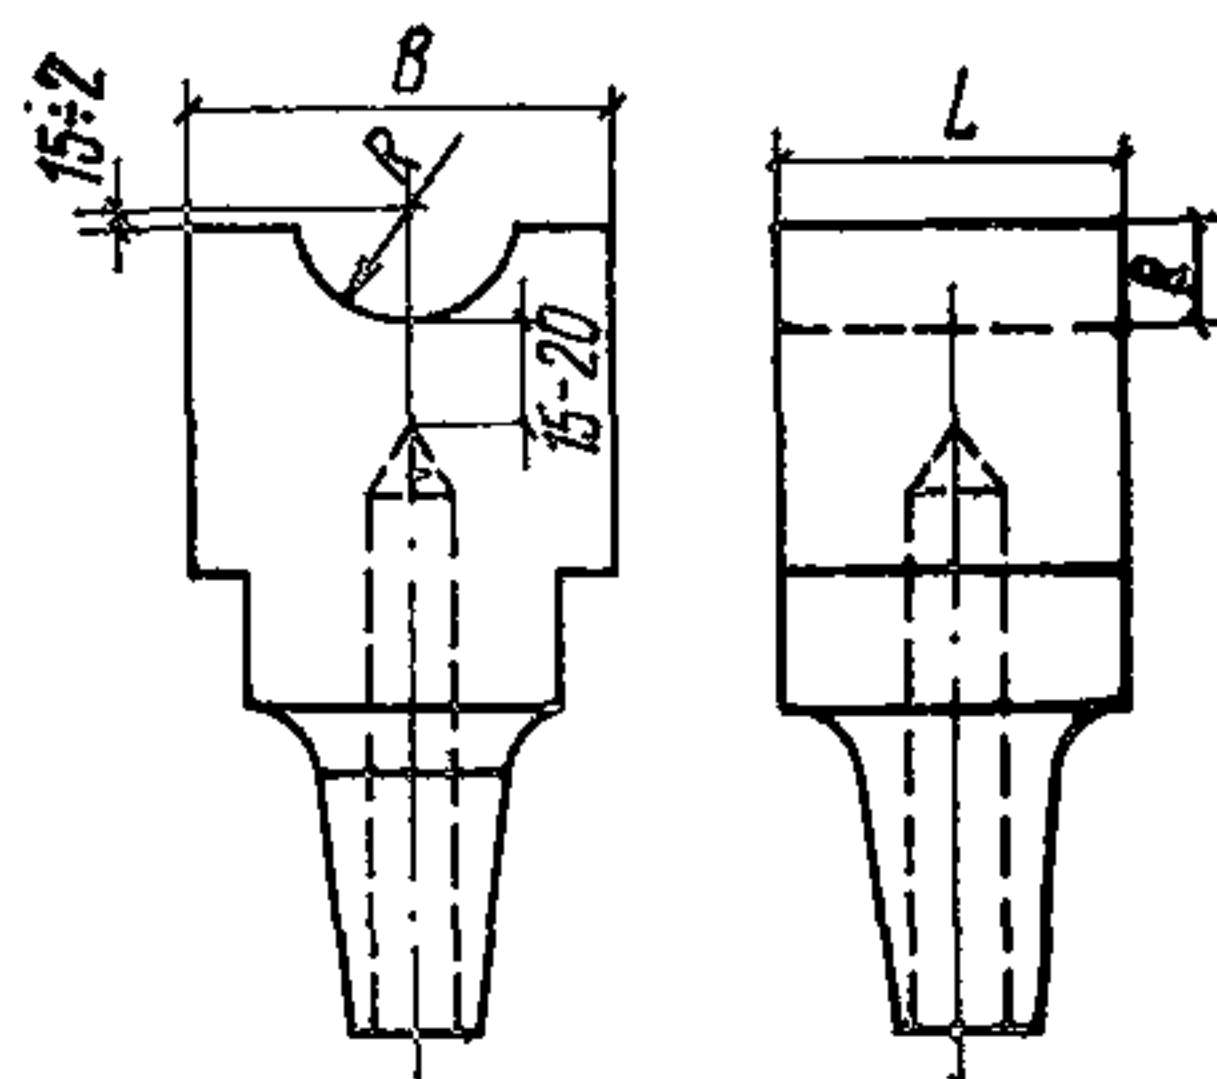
Рекомендуемая форма электродов для контактной сварки внахлестку стыковых соединений арматурных стержней
